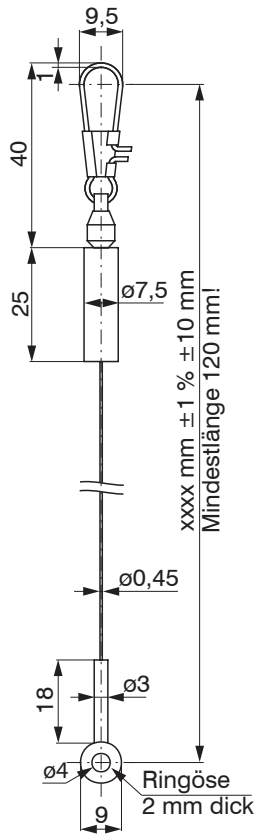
Seilverlängerung WE-xxxx-CLIP, Abmessungen in mm
